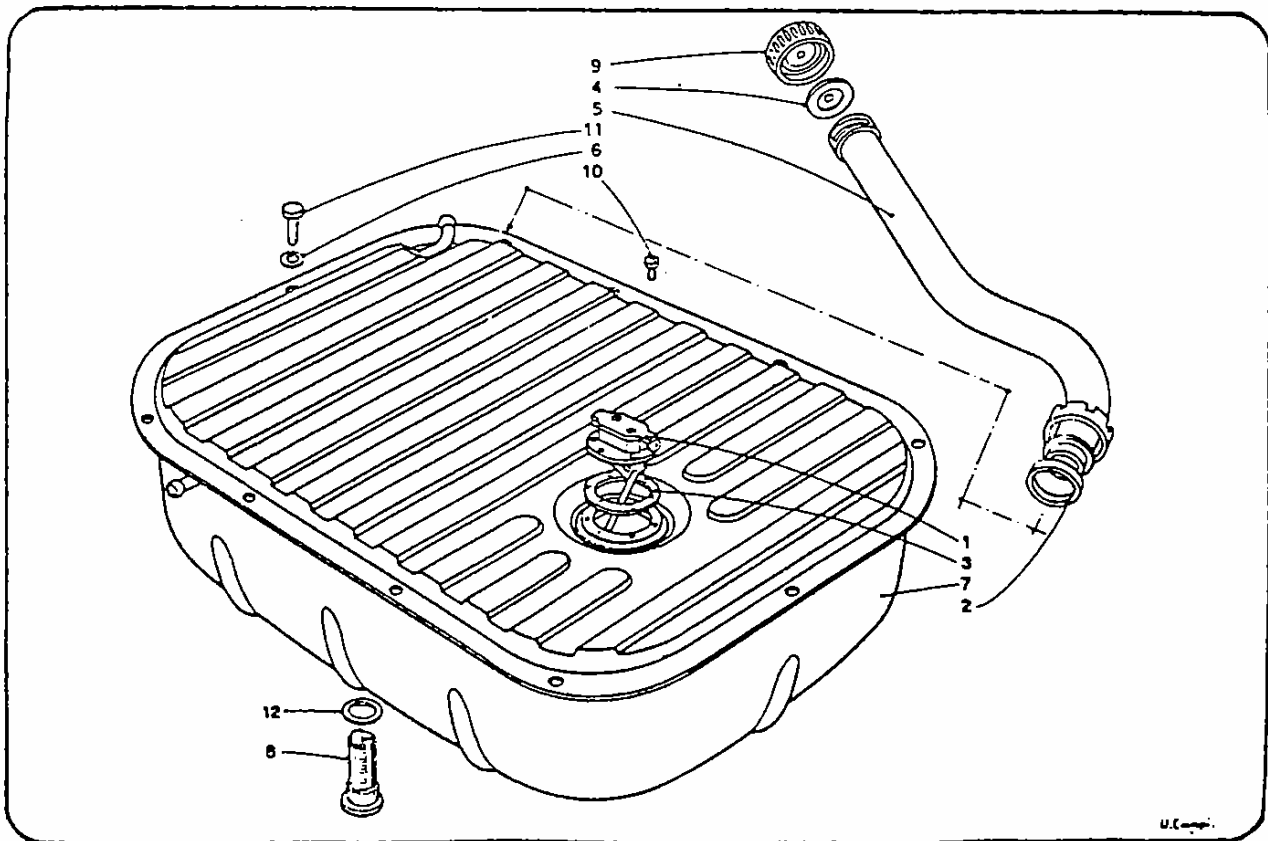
/44 - Réservoir à carburant (du Catalogue Pièces Détachées).
